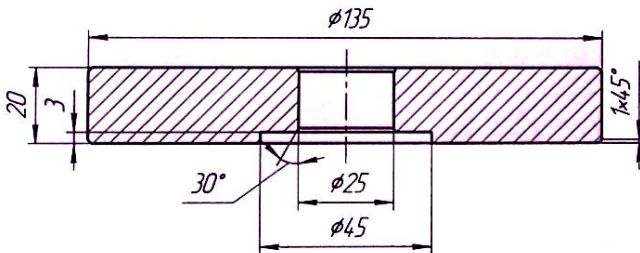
Конструкція і розміри нижньої шайби
